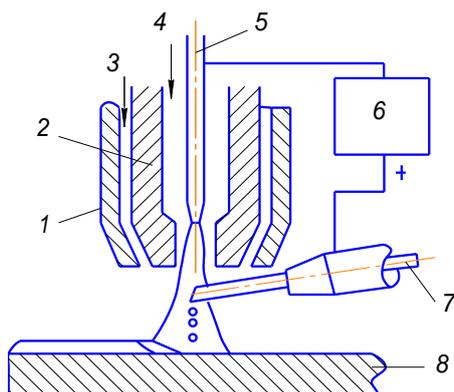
Схема плазменной наплавки струей с токоведущей присадочной проволокой:
